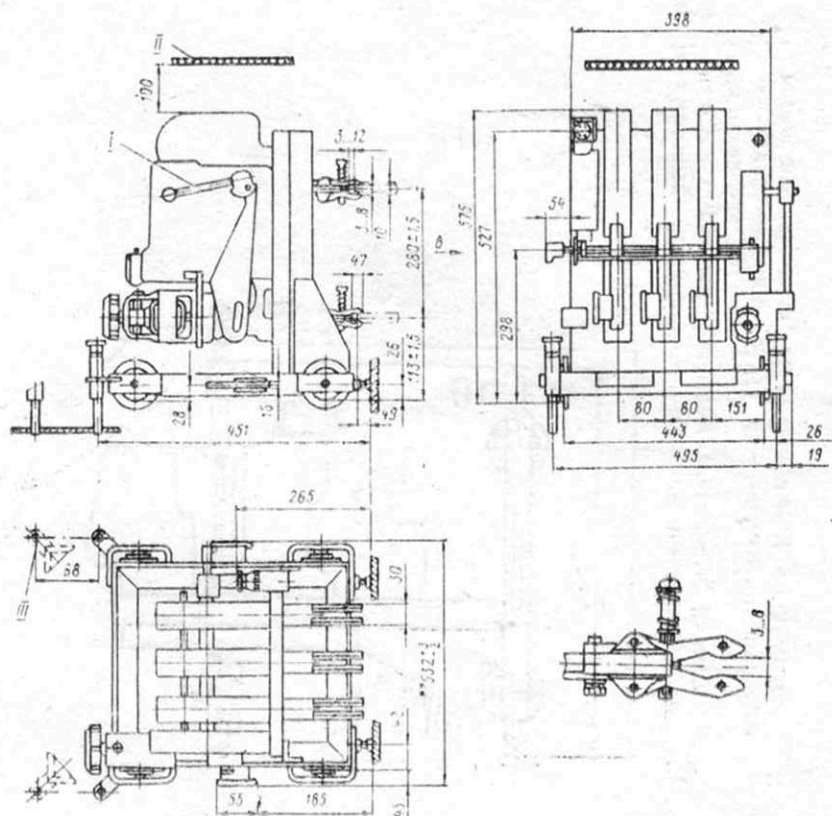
Габаритно-установочные размеры выдвижных выключателей с электродвигательным приводом:
